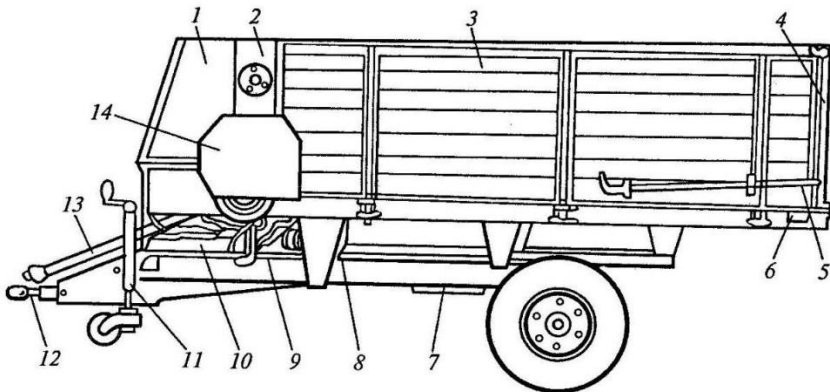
Малогабаритный кормораздатчик РММ – Ф – 6:
